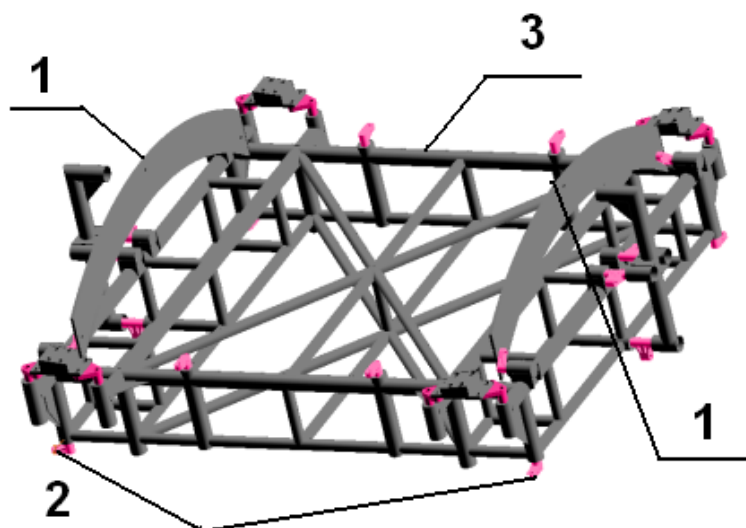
Калібр стику центроплана з фюзеляжем:
